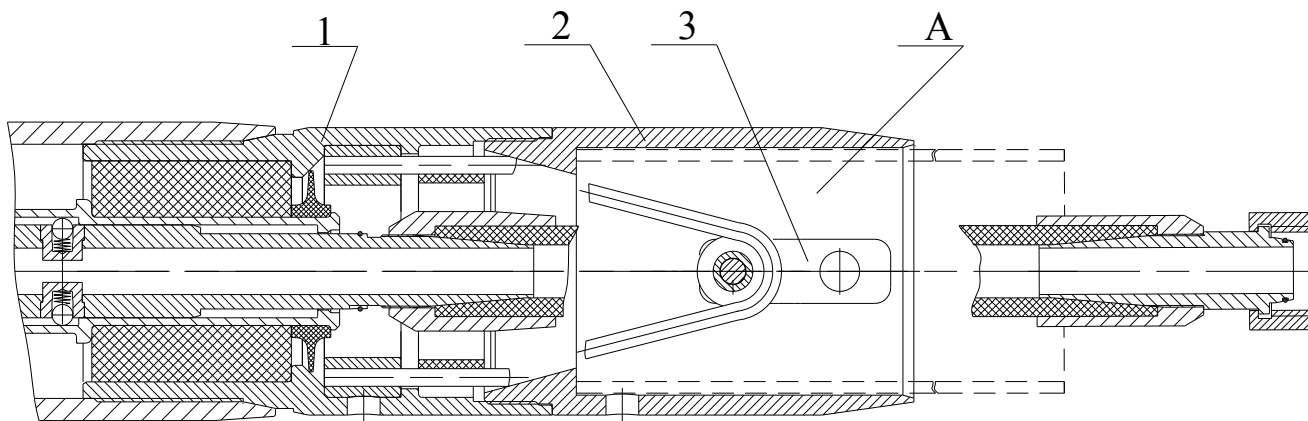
Схема сборки пробойника ИП 4603АМ (по заказу)
